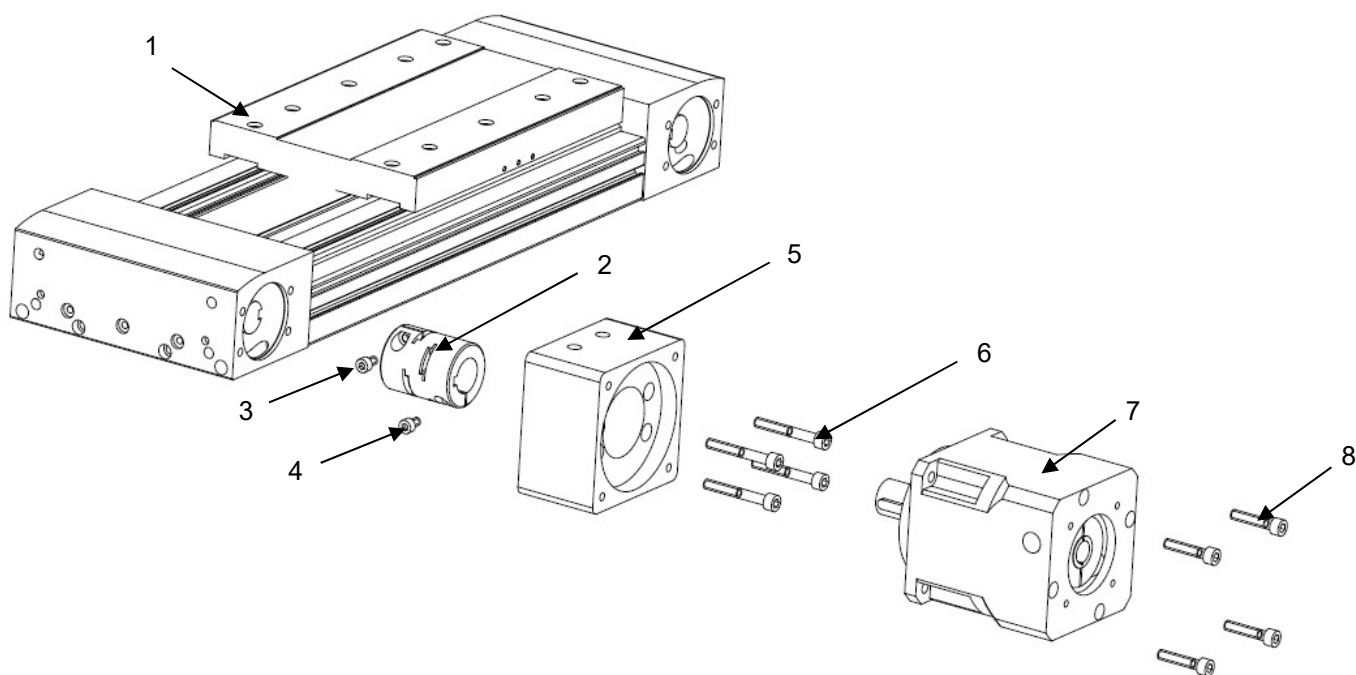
Установка редуктора с помощью монтажного комплекта модели AR-EGT
